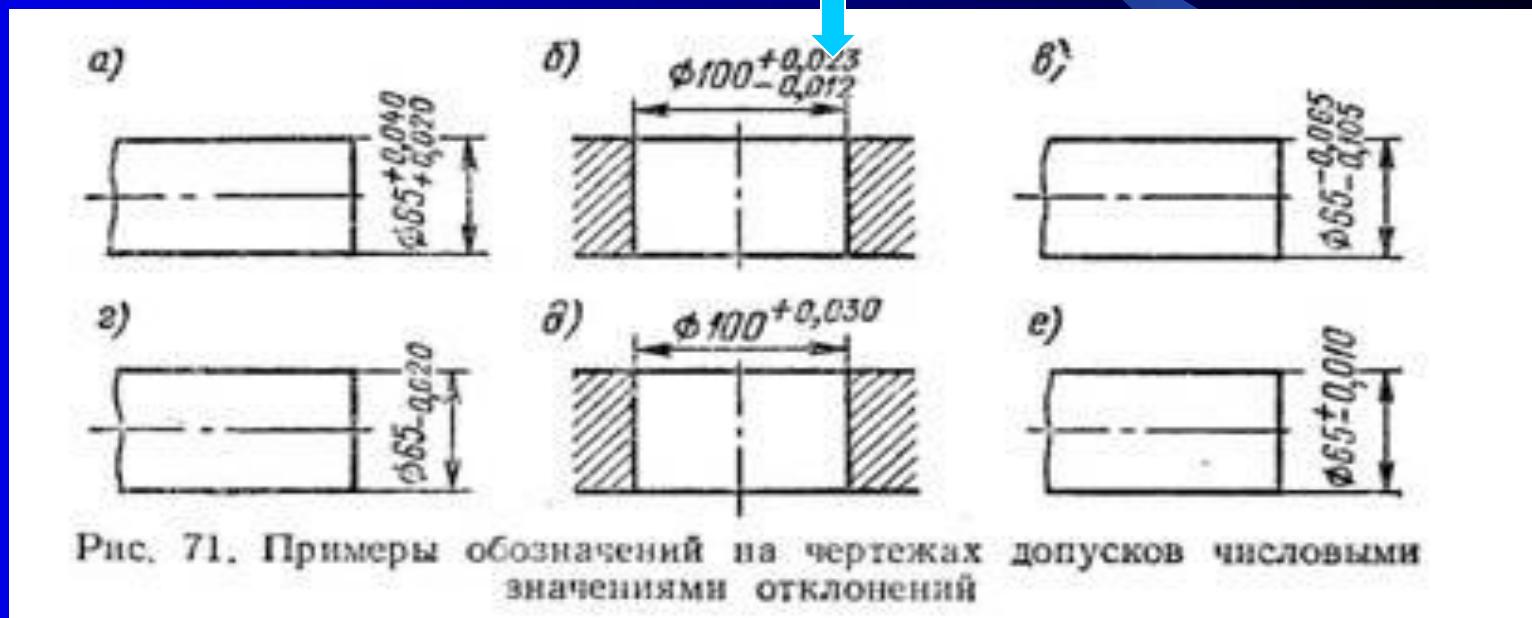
Примеры обозначений на чертежах допусков числовыми значениями отклонений
